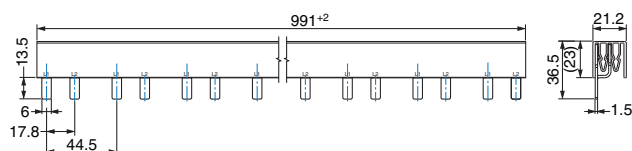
Dimensions de TMC 7...B2...CA (mm)
